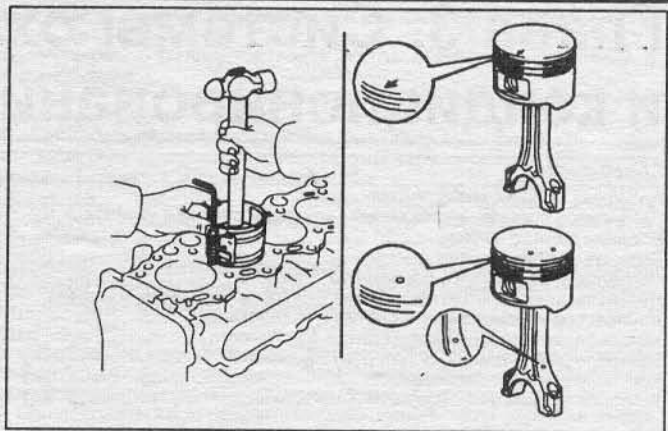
Слева. Установка поршня. Пользуйтесь деревянной или пластиковой рукояткой молотка.
